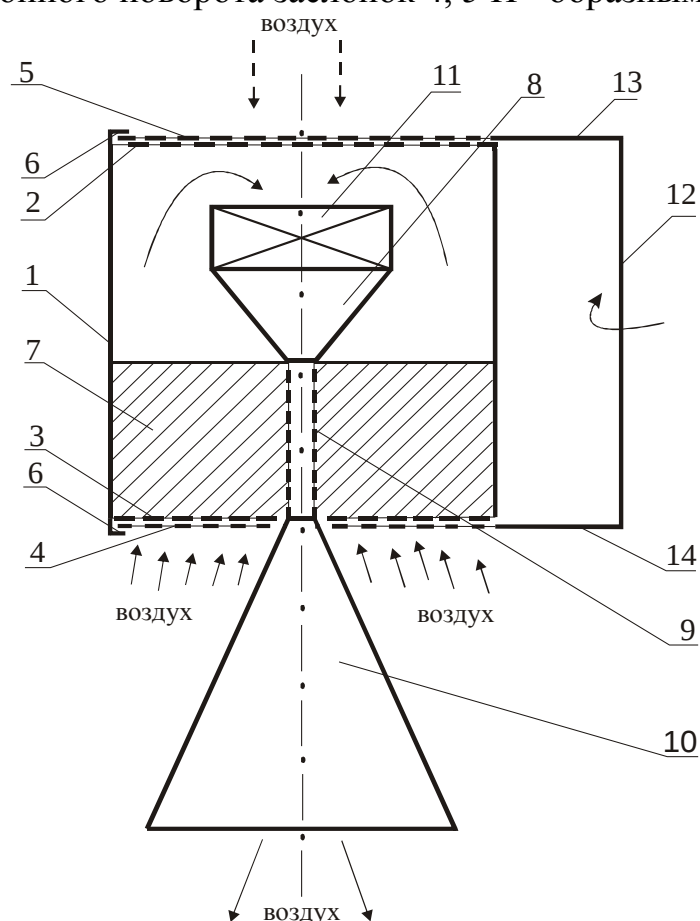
Сушилка для рук и волос: 1 – корпус; 2, 3 – верхняя и нижняя торцевые крышки; 4, 5 – перфорированные заслонки; 6 – желобные каналы; 7 – слой зернистого адсорбента; 8 – конфузор; 9 – перфорированная горловина; 10 – диффузор; 11 – вентилятор; 12 – рычаг; 13, 14 – направляющие
